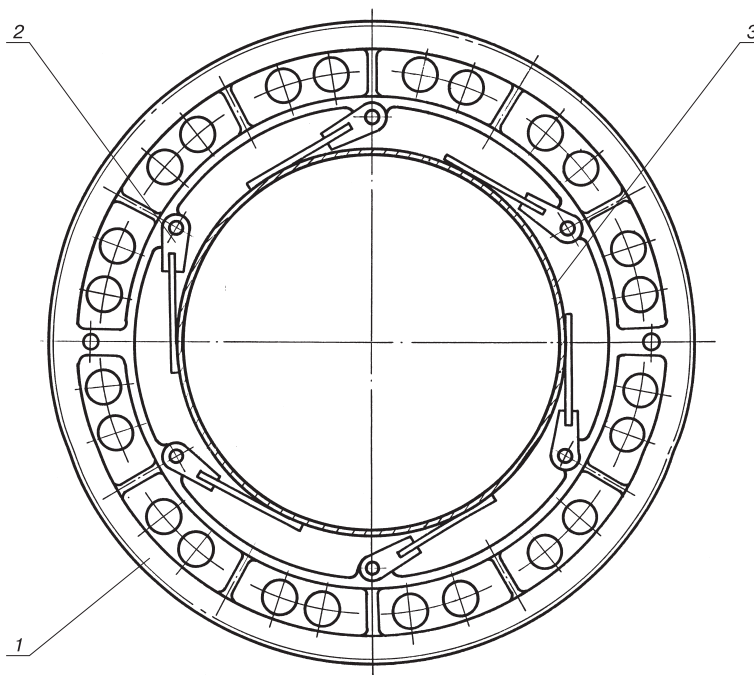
Установка зубчатого венца: 1 – венец зубчатый; 2 – траверса; 3 – обечайка
